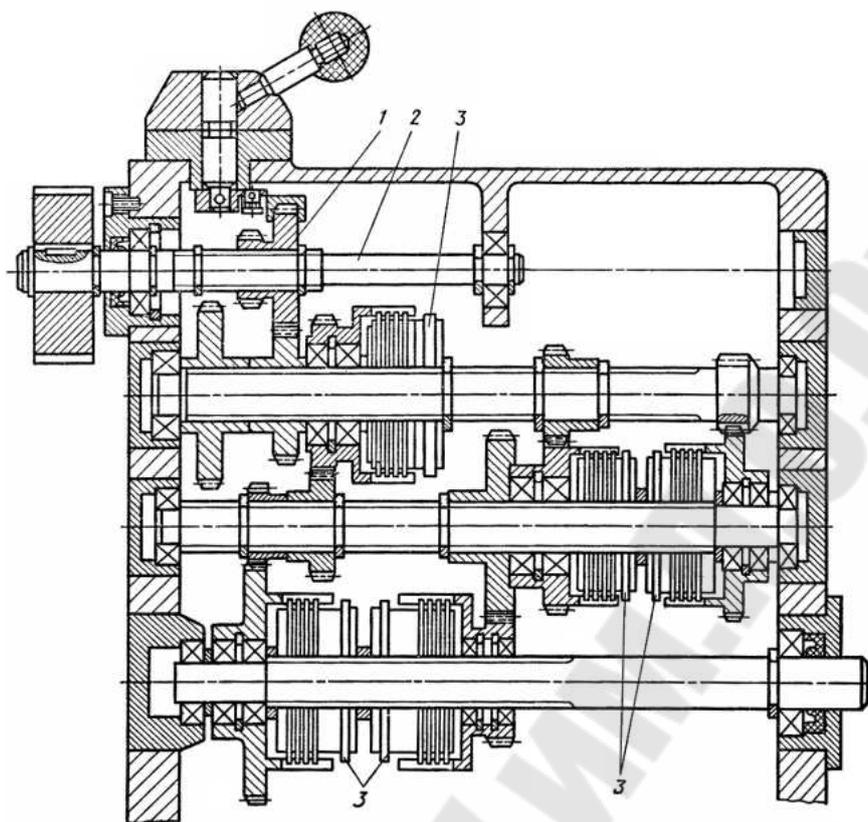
Коробка подачи станка 1Г340П:
